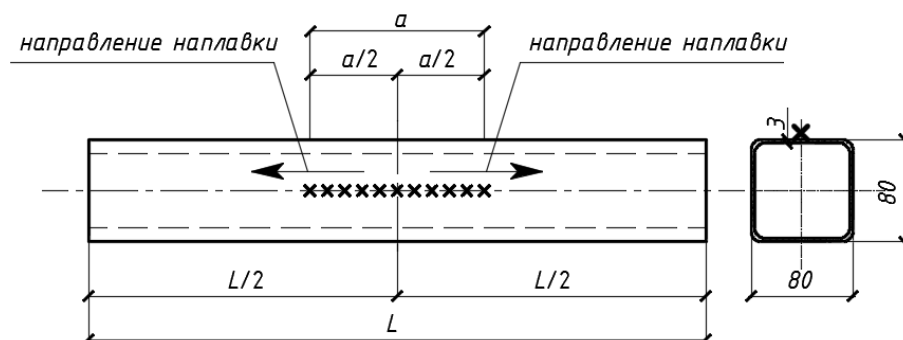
Схема расположения и направления наплавки холостых валиков стальных конструкций из труб квадратного сечения
